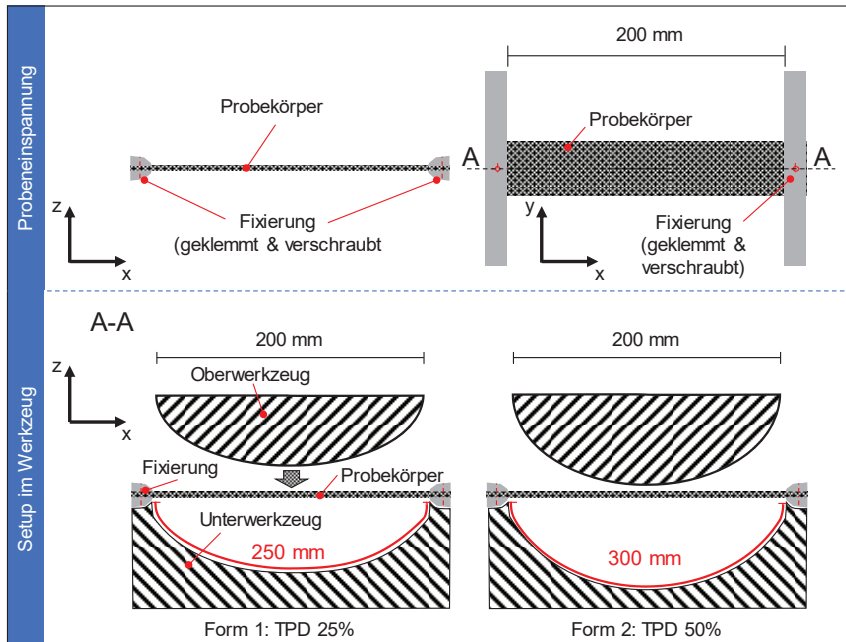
Schema des Spannrahmens und Einbau im Werkzeug
